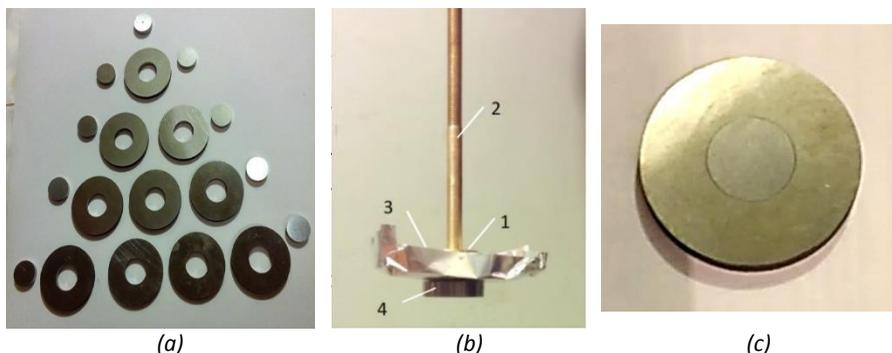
Сборка образцов: (а) диски и кольца перед сборкой, (б) приспособление для введения диска в кольцо, (с) собранный образец.
